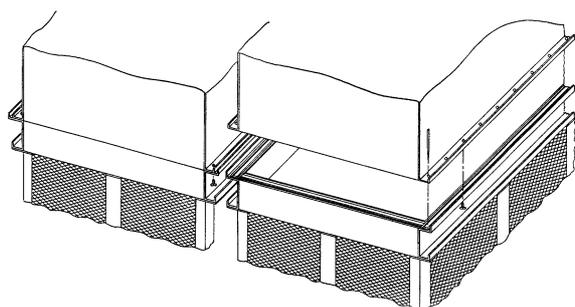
Accoppiamento della sezione ventilante con la sezione bacino
